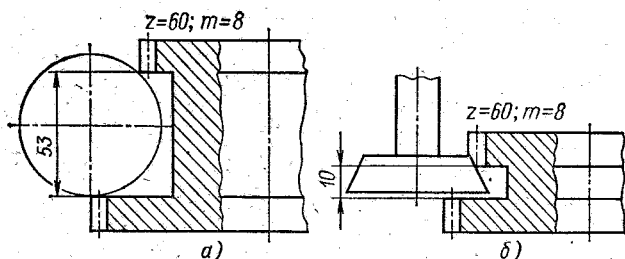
Минимальный выход инструмента при нарезании блочных колес:
